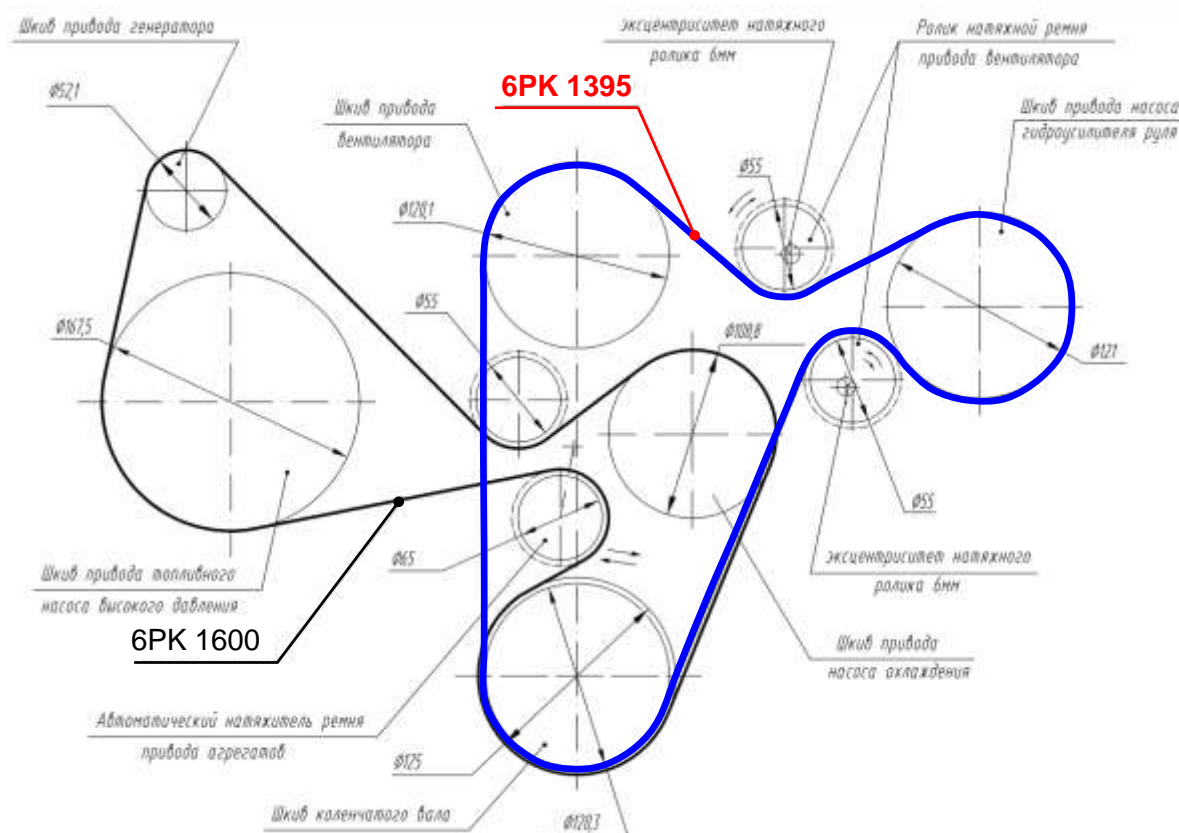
Схема привода вспомогательных агрегатов двигателя для автомобилей на платформе УАЗ-3163 без компрессора кондиционера
